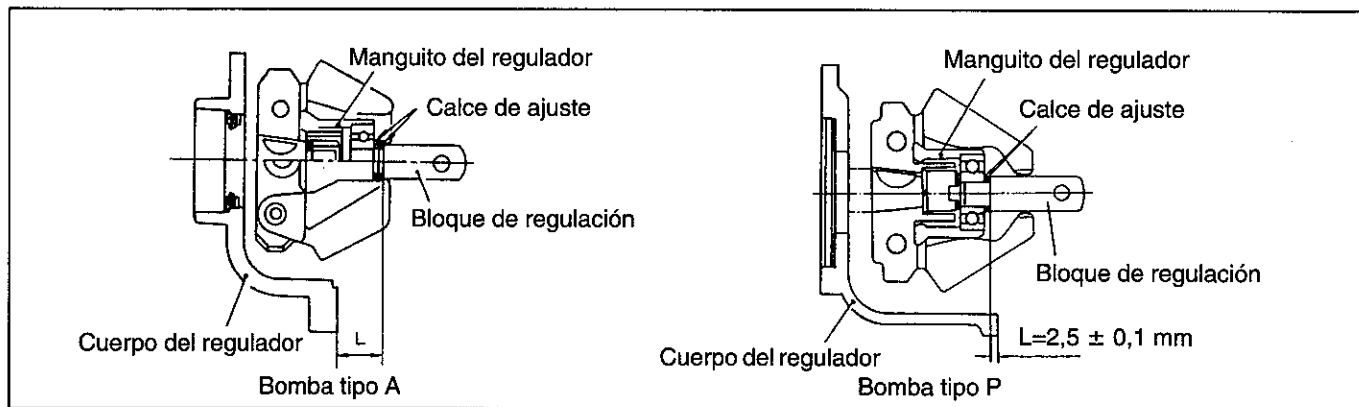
Dimensiones para el conjunto del bloque de regulación
